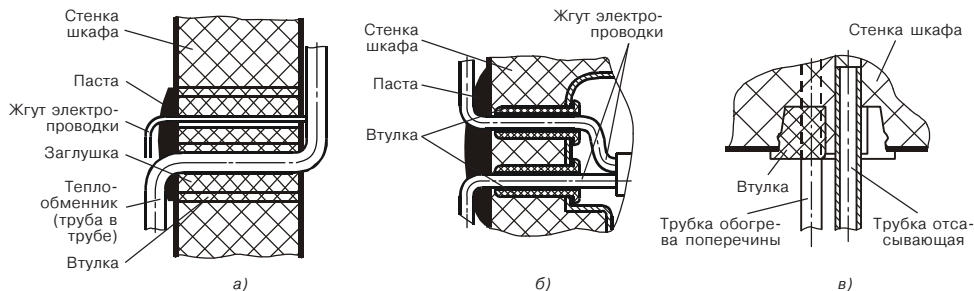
Вывод трубопроводов холодильного агрегата и жгутов электропроводки через стенки шкафа
